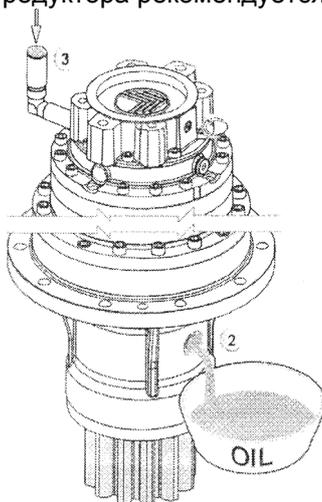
Схема залива и слива масла из редуктора и контроля уровня.
